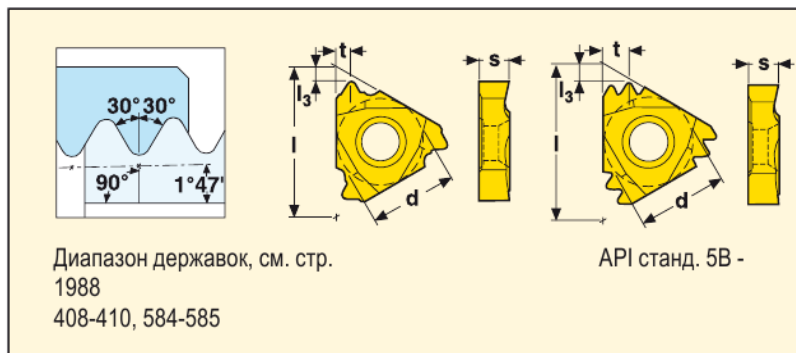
Горизонтальний і фронтальний вигляд твердосплавних пластин фірми SECO для нарізання трикутної різьби за API 5B
